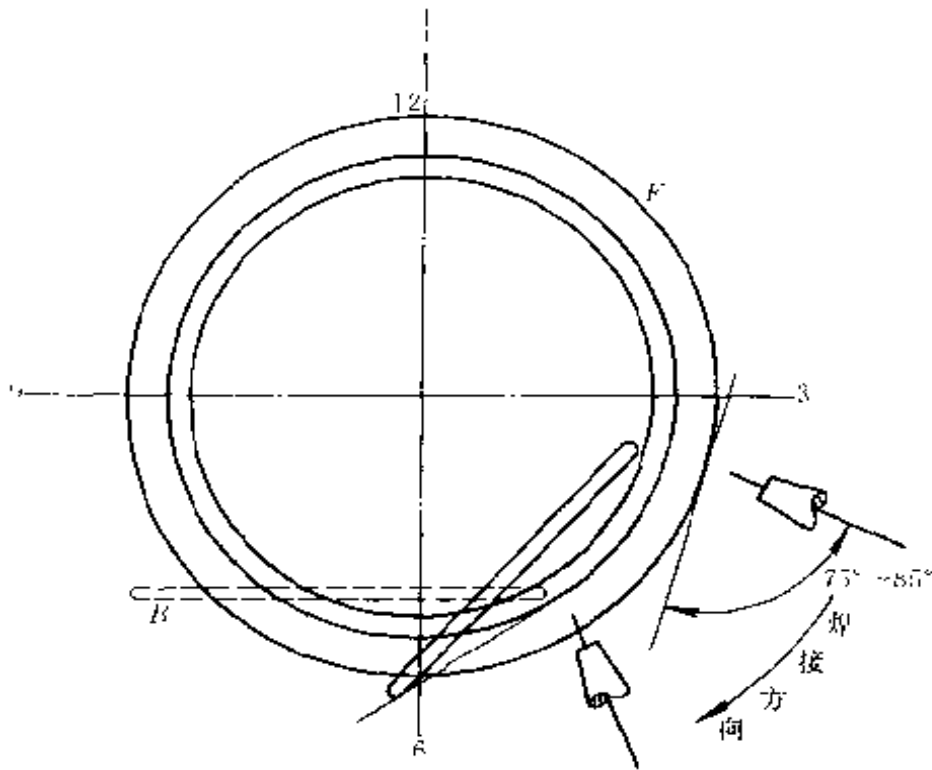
小管水平固定对接时钟 3 点位置至 6 点位置焊缝的手工 TIG 焊
